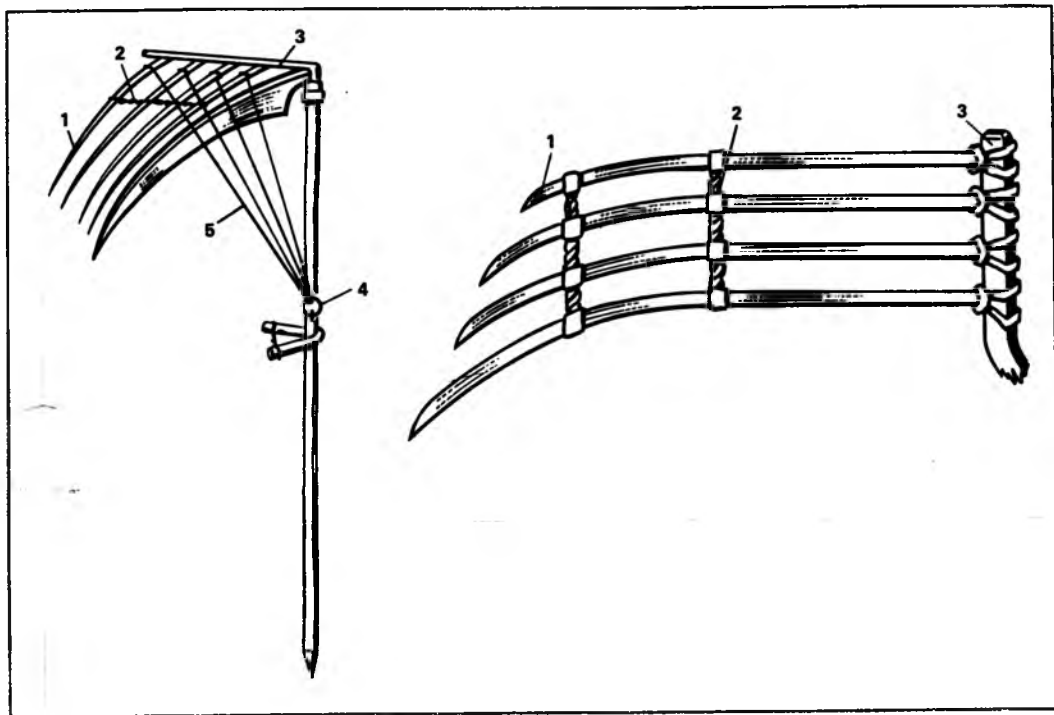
Коса с легкими грабельками: 1 — зуб; 2 — сыромятный ремень; 3 — квадратный брус; 4 — кольцо; 5 — бечевка
